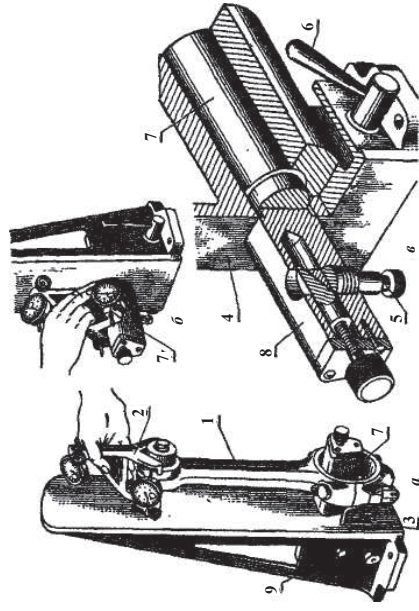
Прибор КИ-724 для проверки шатунов:
